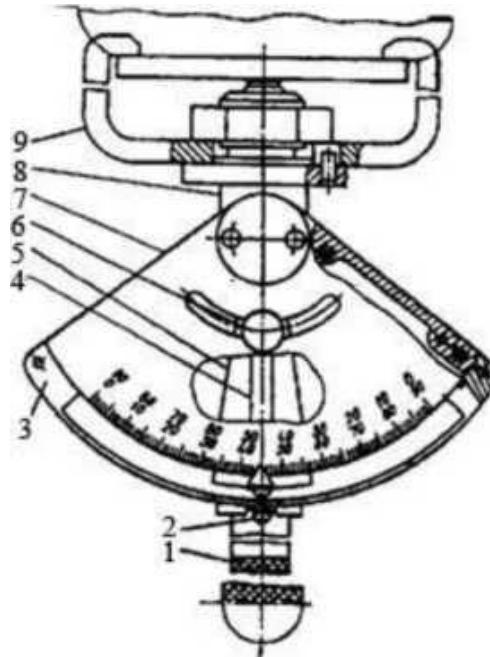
Загальний вигляд пристрою для визначення величини зазорів у головних передачах та карданних валах КИ-6314:
